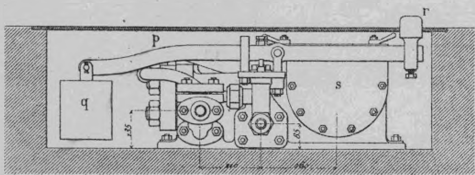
Elevation latérale s^t IJ (Fig 6)
